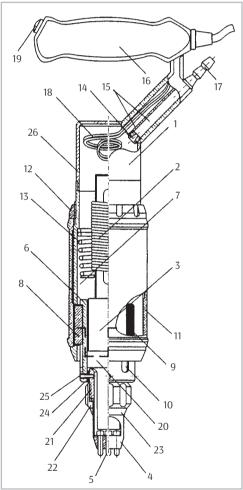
Конструкция ультразвукового виброударного инструмента: 1 — корпус; 2 — пьезоэлектрический преобразователь; 3 — волноводный акустический трансформатор; 4 — обойма-держатель бойков; 5 — бойки; 6 — втулка-держатель источника возбуждения; 7 — зазор; 8 — направляющие скольжения; 9, 10 — пазы для закладки направляющих; 11 — кожух; 12 — гайка; 13 — пружинный амортизатор; 14 — дроссель; 15 — канал для сжатого воздуха; 16 — рукоятка; 17 — штуцер; 18 — провода питания преобразователя; 19 — гашетка; 20 — фланец; 21 — переходная втулка; 22 — накидная гайка; 23 — стопорное кольцо; 24 — эластичная манжета; 25 — шпильки; 26 — разъемное соединение
